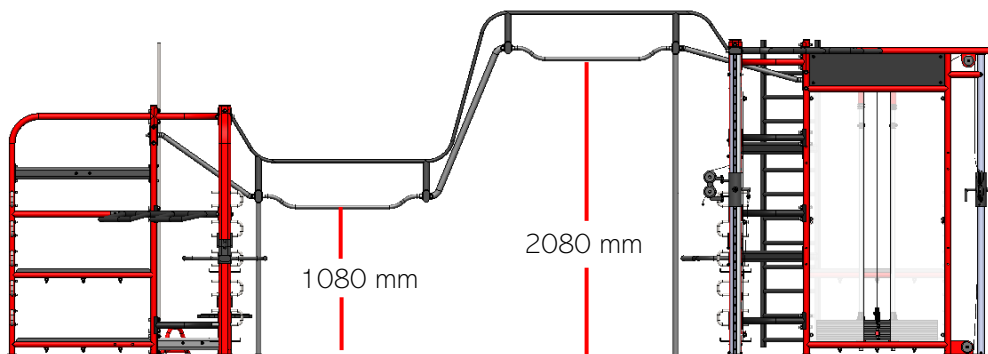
Módulo 5 unido al conjunto, vista de perfil. Fuente: Elaboración propia
